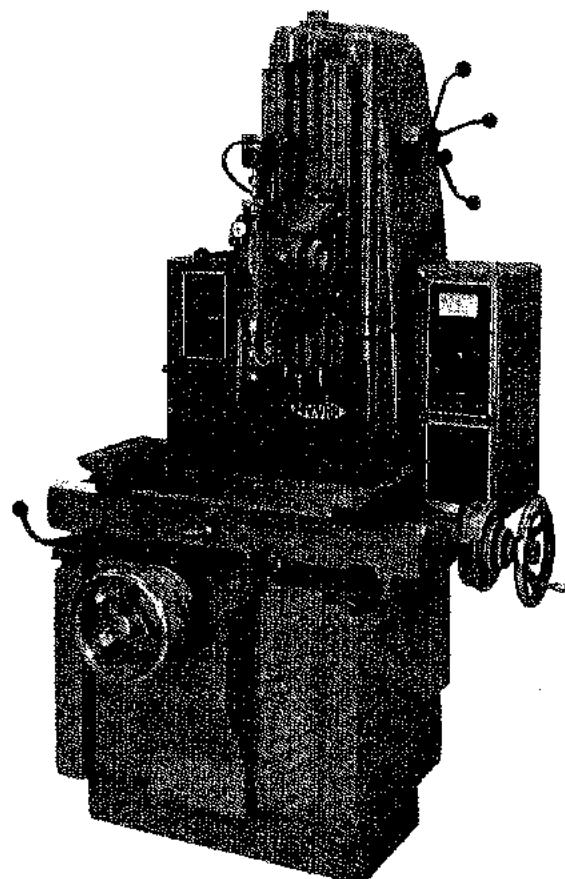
Máquina de medir de precisión (Moore Special Tool Co., Inc.)
